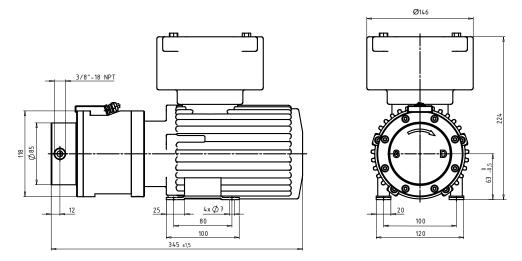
Abmessungen Mikrozahnringpumpe mzr-11557 Ex (Gesamtlänge abhängig vom Motortyp)
